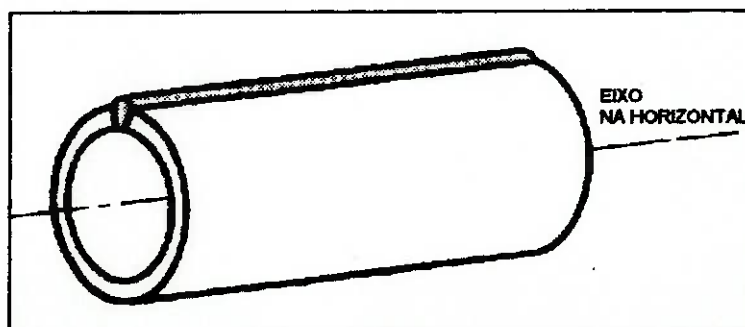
Posição de soldagem da junta longitudinal do casco cilíndrico
